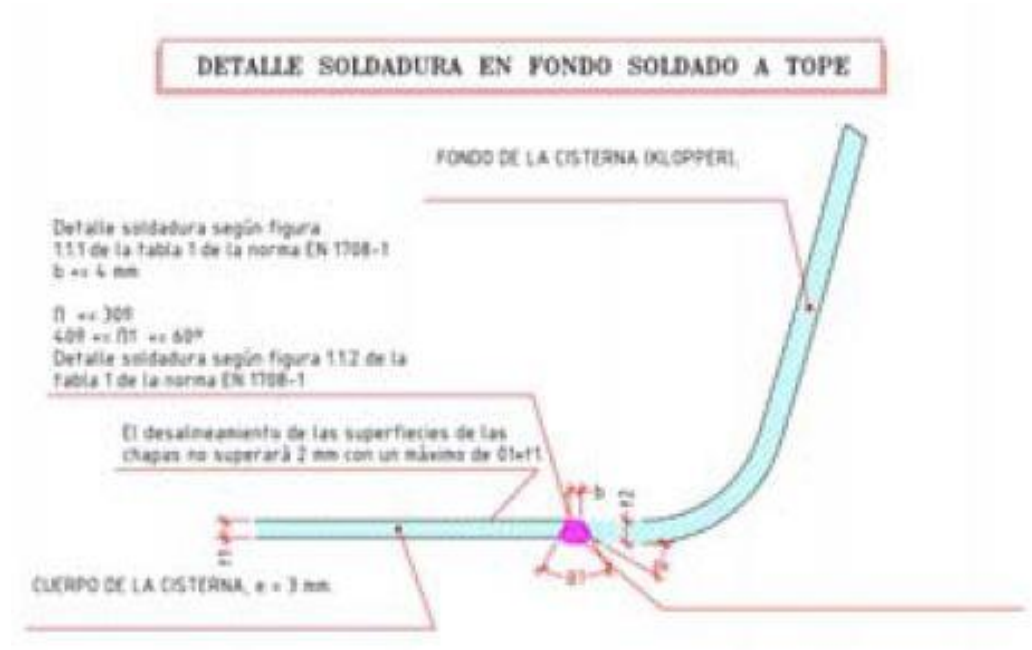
Detalle soldadura en fondo soldado a tope
